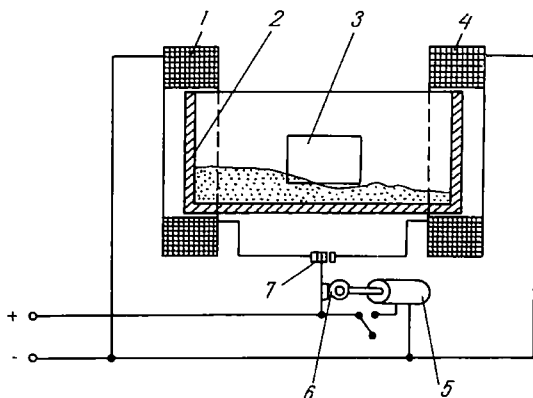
Схема устройства для обработки крупногабаритных деталей
